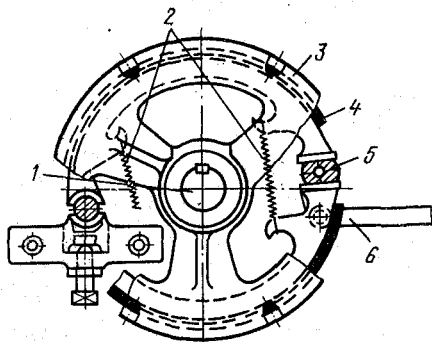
Схема тормоза главного вала станка АТ-100-5
